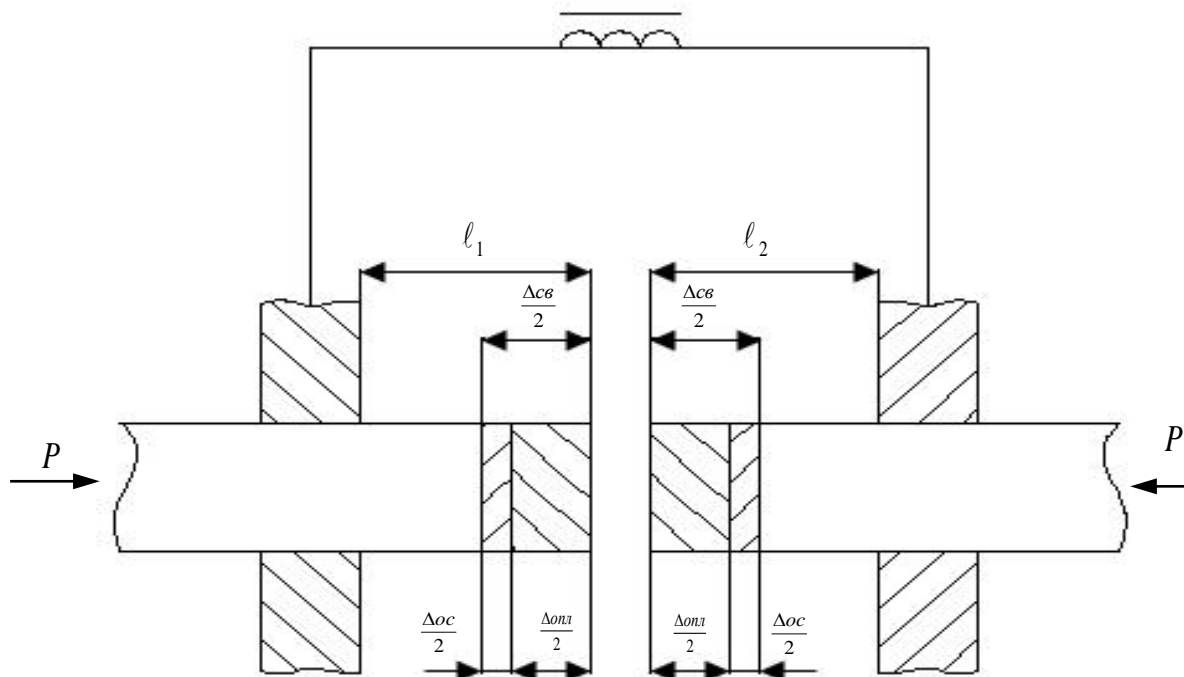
Схема процесса стыковой сварки оплавлением
